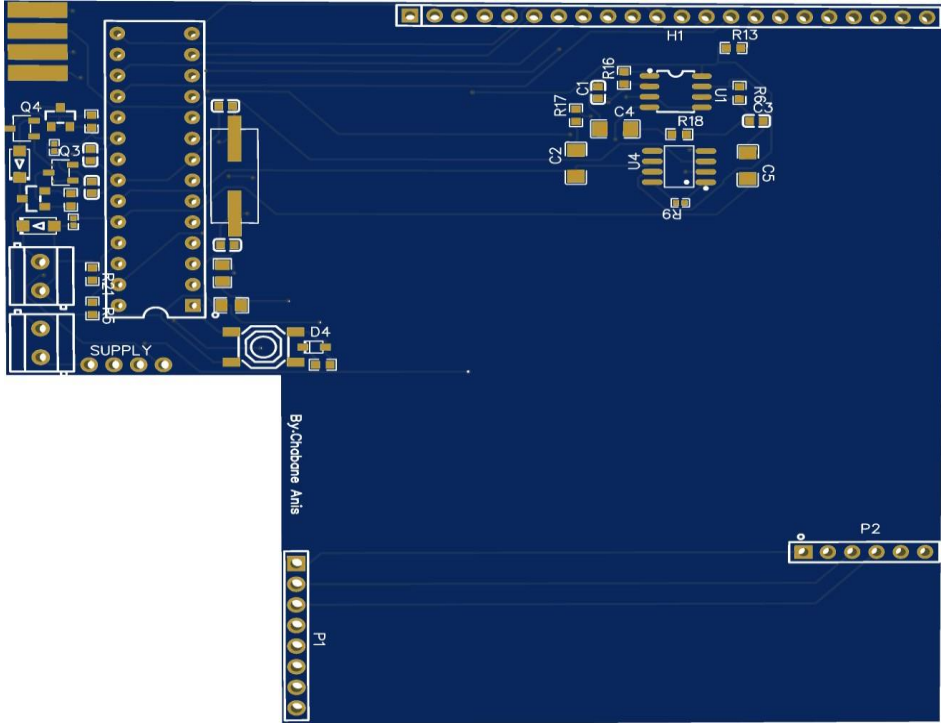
Vue de dessus de la disposition du PCB sans composants
